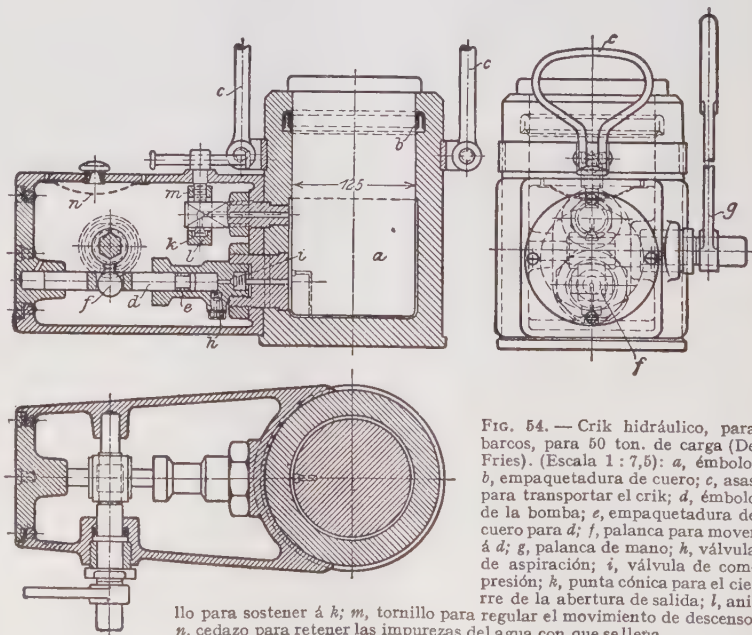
Crik hidráulico, para barcos, para 50 ton. de carga (De Fries). (Escala 1:7,5): a , émbolo; b , empaquetadura de cuero; c , asas para transportar el crik; d , émbolo de la bomba; e , empaquetadura de cuero para d ; f , palanca para mover á d ; g , palanca de mano; h , válvula de aspiración; i , válvula de compresión; k , punta cónica para el cierre de la abertura de salida; l , anillo para sostener á k ; m , tornillo para regular el movimiento de descenso; n , cedazo para retener las impurezas del agua con que se llena
